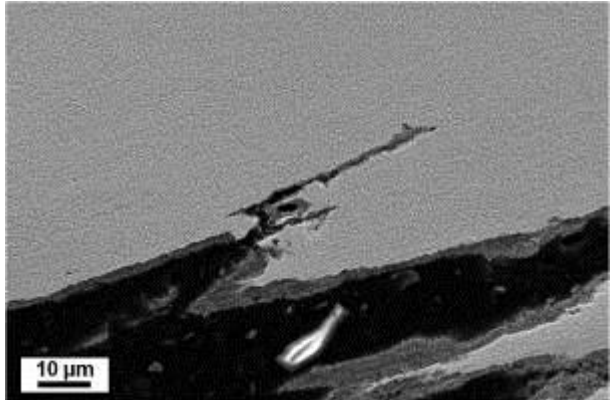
Acier 2 : Observation dans le plan DL-TC d'une fissure secondaire
